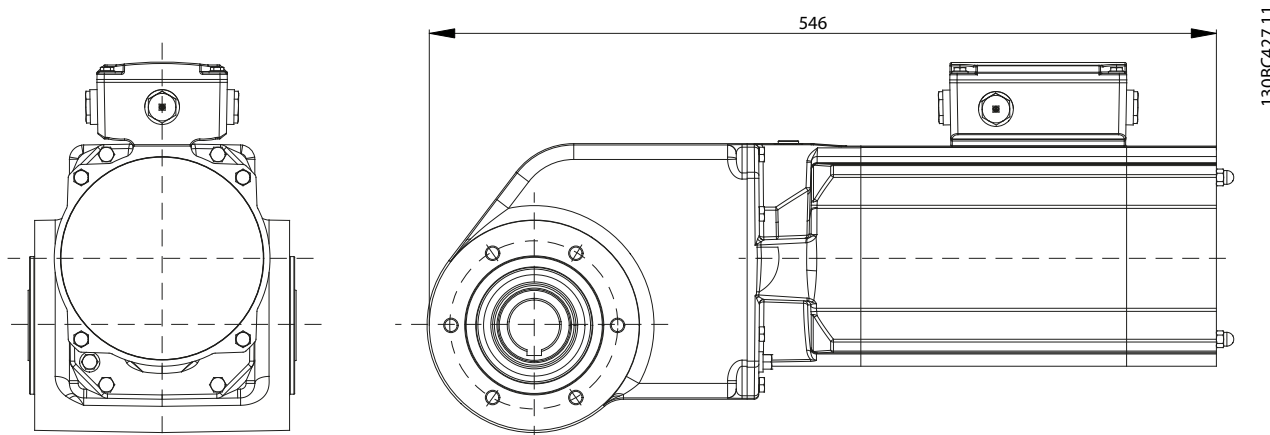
Dimensões: OneGearDrive™ com freio mecânico opcional
